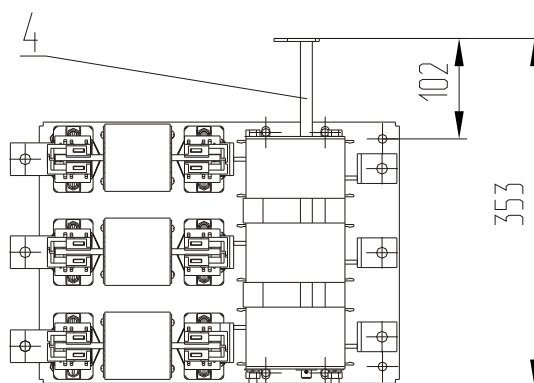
Выключатель-разъединитель-предохранитель ВРП-37-31201-00УХЛ3 с боковой смещенной рукояткой привода зависимого действия и приводным валом слева.
